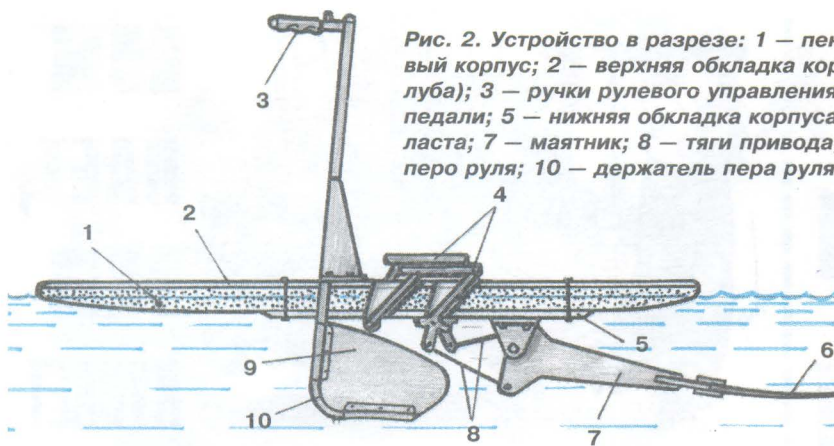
Устройство в разрезе: 1 — пенопластовый корпус; 2 — верхняя обкладка корпуса (палуба); 3 — ручки рулевого управления; 4 — педали; 5 — нижняя обкладка корпуса; 6 — ласта; 7 — маятник; 8 — тяги привода; 9 — перо руля; 10 — держатель пера руля.
